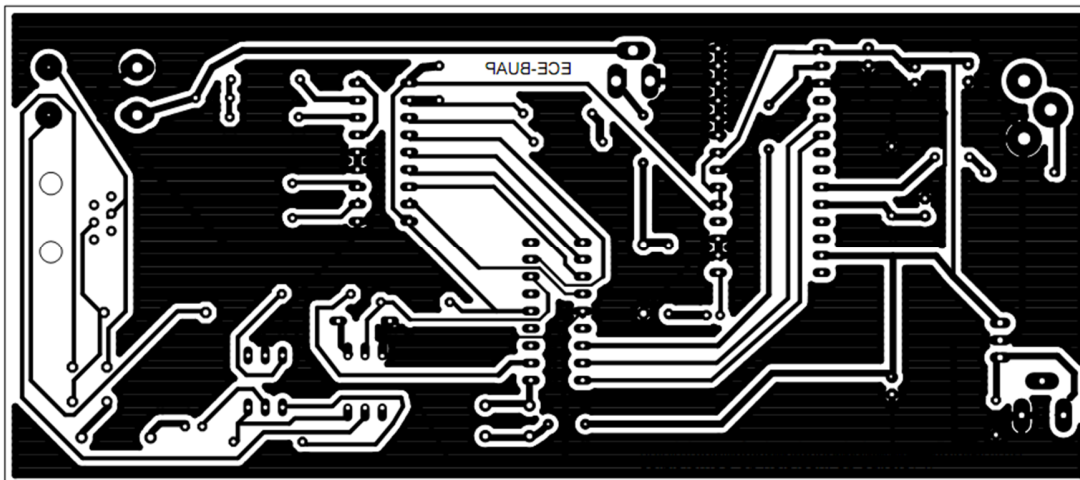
Diseño de la placa de circuito impreso, lado de soldaduras. (No está a tamaño real)
